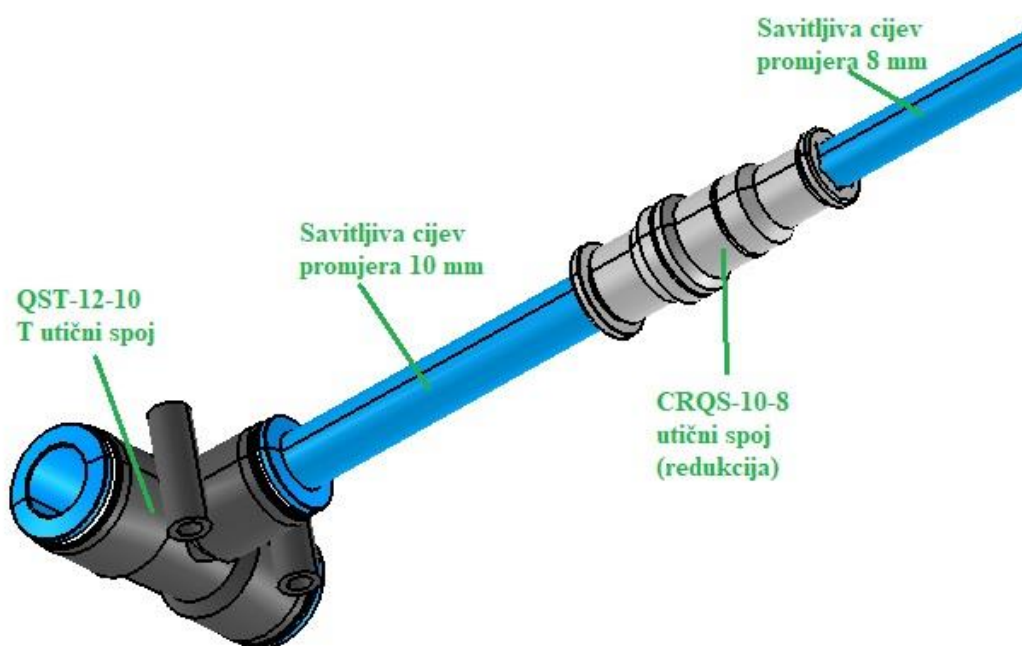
3D CAD model senzora pozicije sa pripadajućim komponentama [8]
